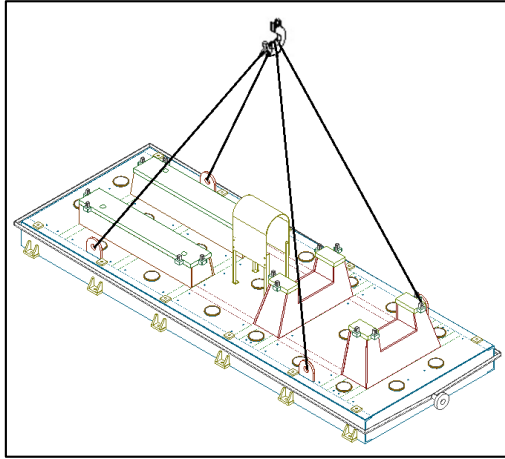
Levantamiento de la placa base desde las orejas de izaje sin equipo de bombeo montado.
